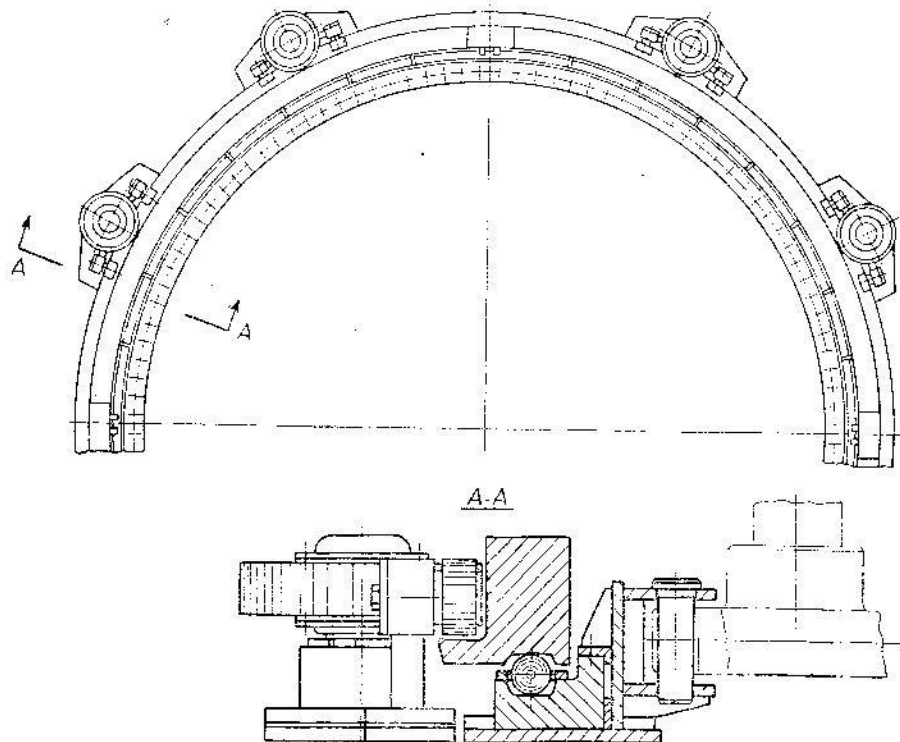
Опорно-поворотное устройство с коническими катками:
